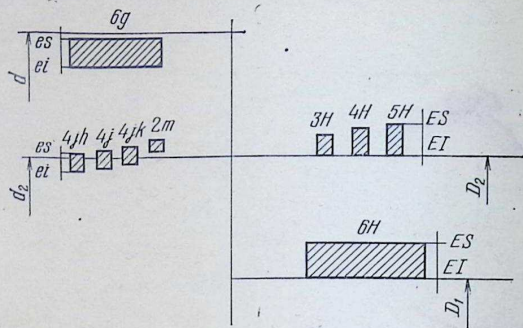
Расположение полей допусков резьб с переходными посадками.
